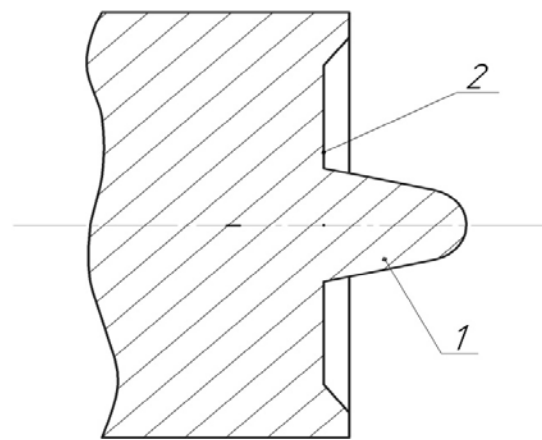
Схематичне зображення робочого інструмента для зварювання тертям із перемішуванням: 1 – штифт; 2 – поверхня плеча
